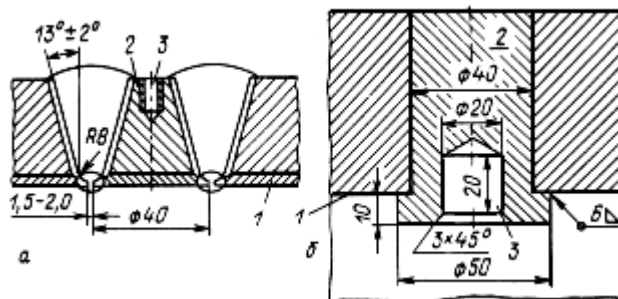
Ремонт сквозного отверстия: а - в штуцере из двухслойной стали; б - в стенке аппарата; 1 - стенка штуцера или аппарата; 2 - заглушка; 3 - отверстие для крепления сборочных приспособлений (после заварки заглушки закрывается металлической пробкой с резьбой соответствующих размеров)
